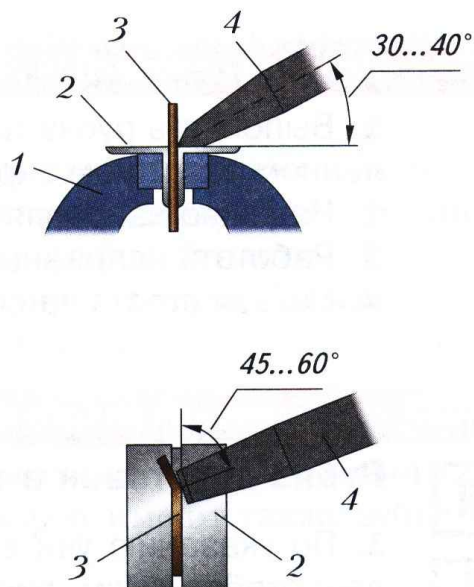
Положение зубила при рубке в тисках: 1 – тиски; 2 – нагубники; 3 – заготовка; 4 – зубило
